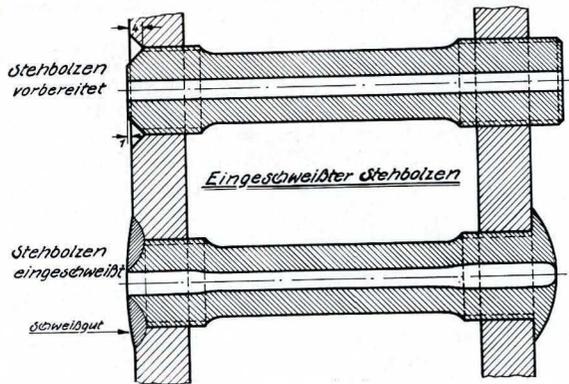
In die Feuerbüchswand autogen eingeschweißte Stehbolzen (Reichsbahn- ausbesserungswerk Cottbus)
